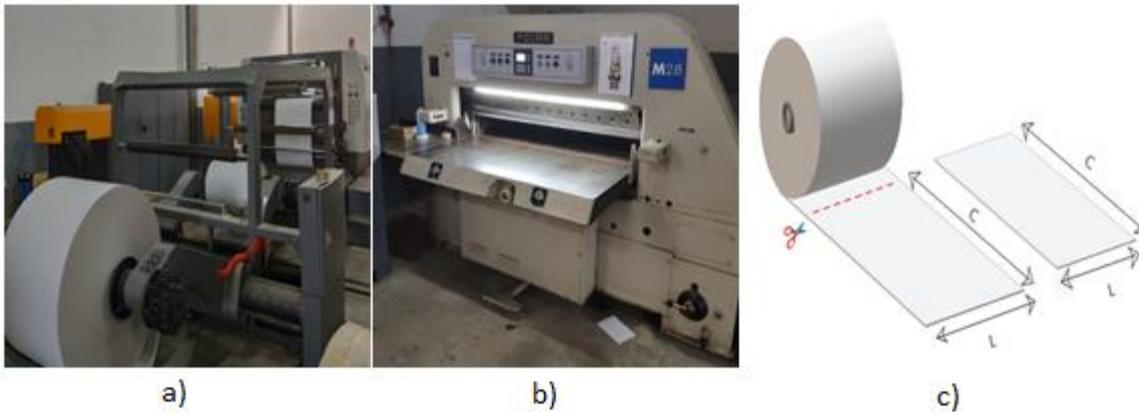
a) Máquina automática de Corte; b) Guilhotina; c) Corte da Bobina em planos
